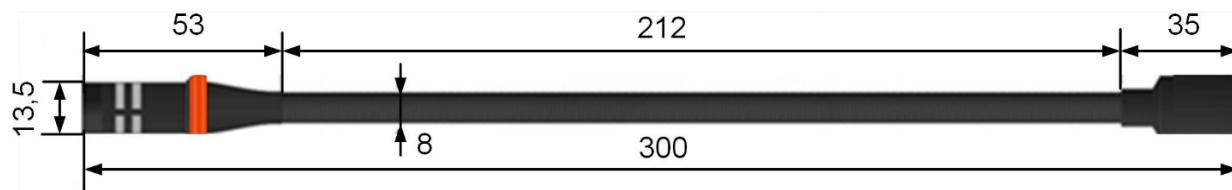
Внешний вид и габаритные размеры микрофона G14-2
